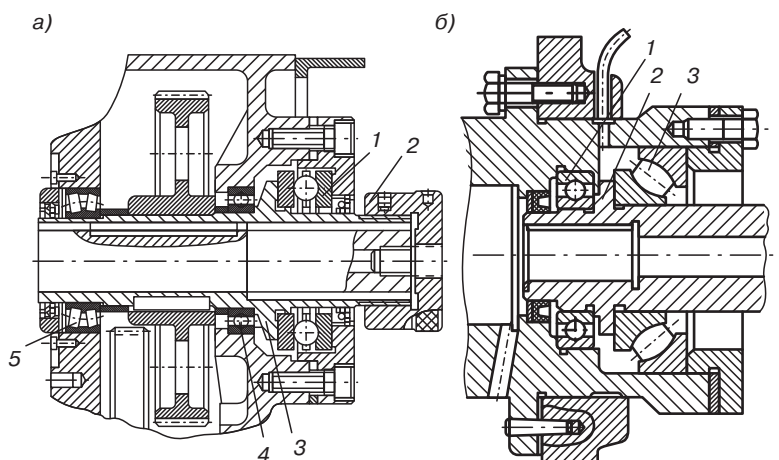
Примеры схем установки подшипников в опорах шнека
